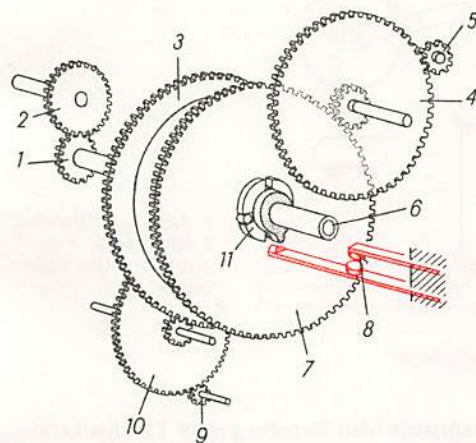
Aufzugsteuerung eines Uhrwerks über ein Stirnradgetriebe
